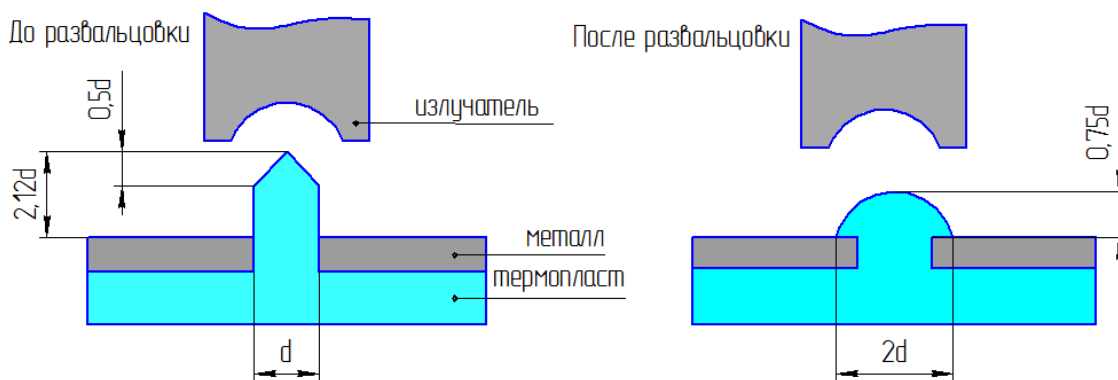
Схема ультразвуковой развальцовки заклепок
